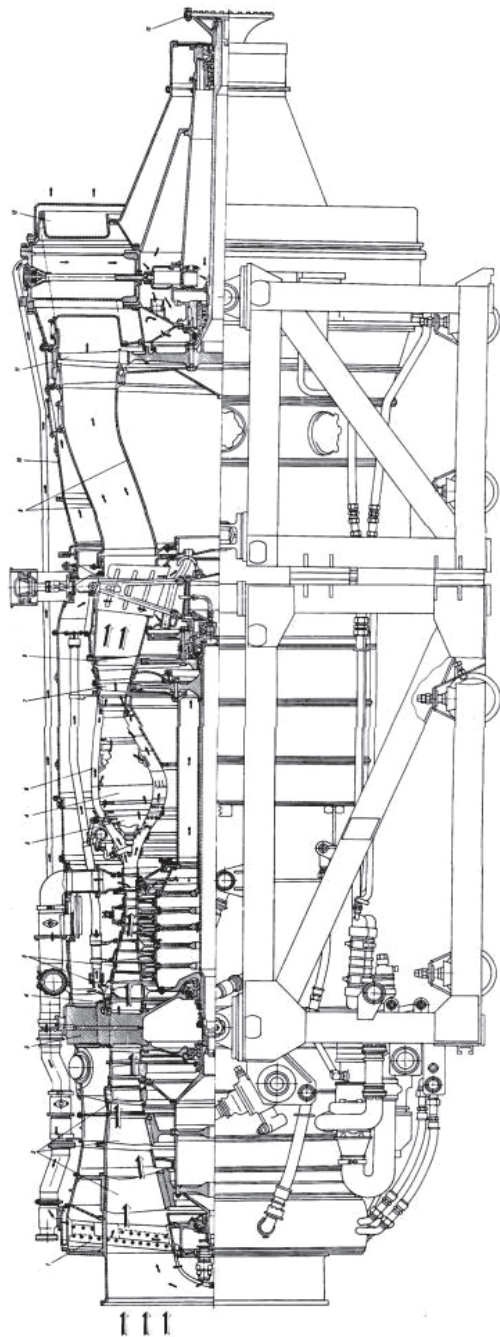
Газотурбинный двигатель НК-16СТ:
